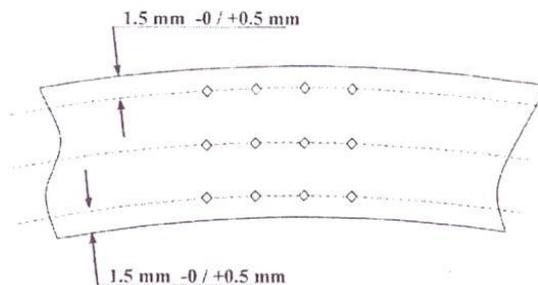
Измерение твердости основного металла сварных и тела бесшовных труб
